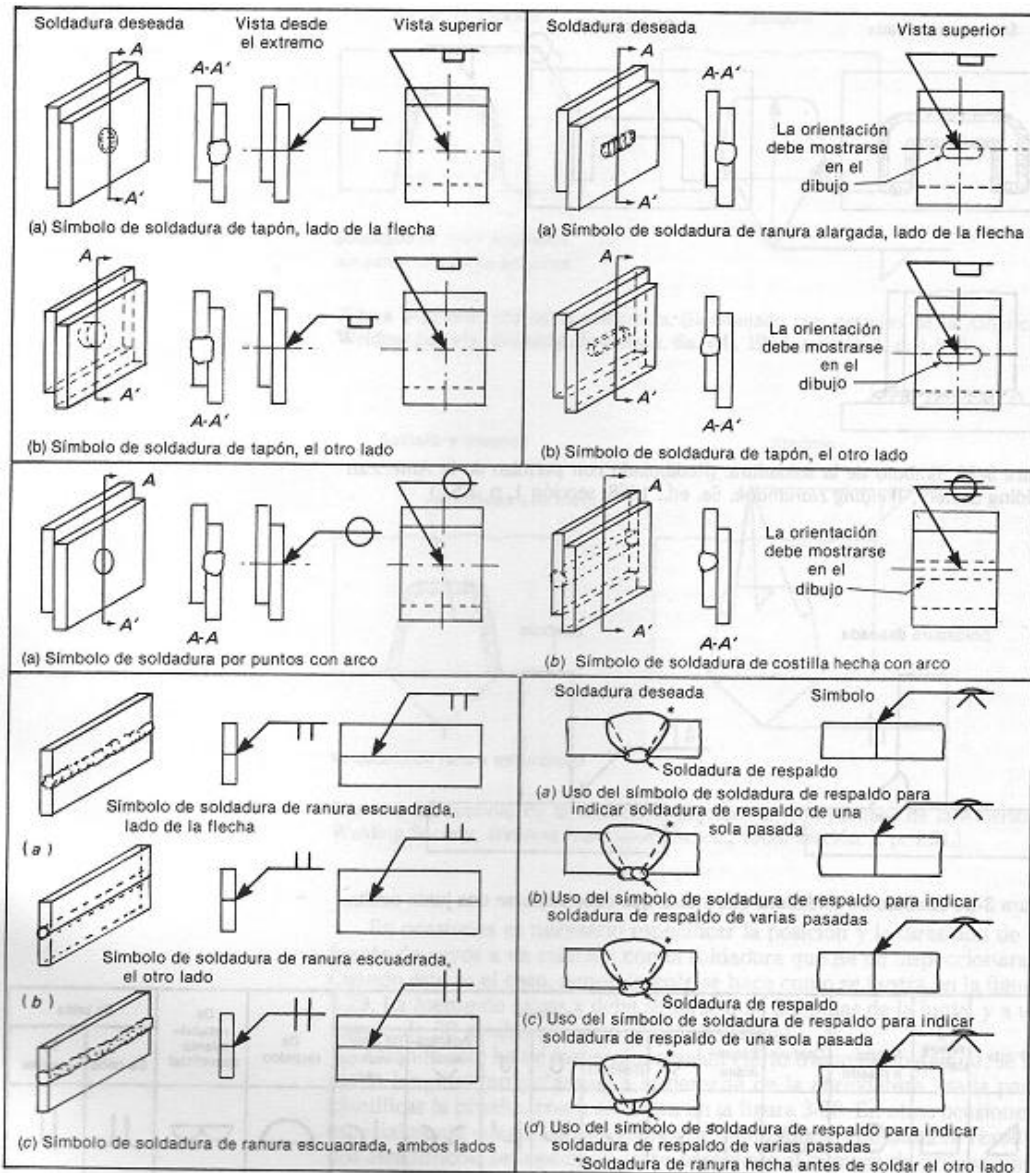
Ejemplos de símbolos de soldaduras y las soldaduras que representan.
